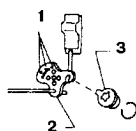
Положение установки коленчатого рычага левой задней двери (См. Раздел 13)
